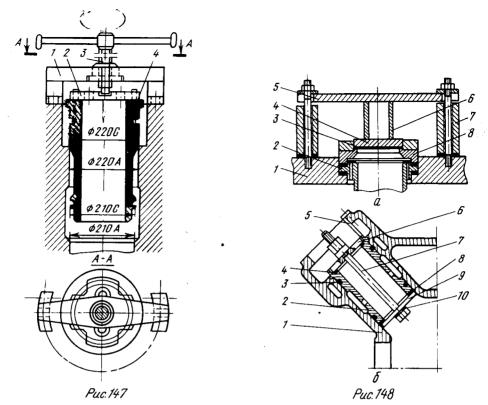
Приспособление для запрессовки гильз в блок-картер: l — скоба приспособления; 2 — нажимной диск; 3 — винт; 4 — гильза
